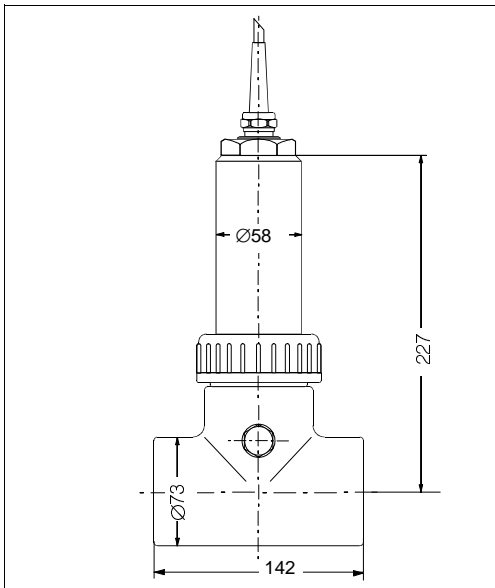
Dimensions de la chambre de passage CUA 250-B pour le montage par raccord fileté Ø63 (à coller)
